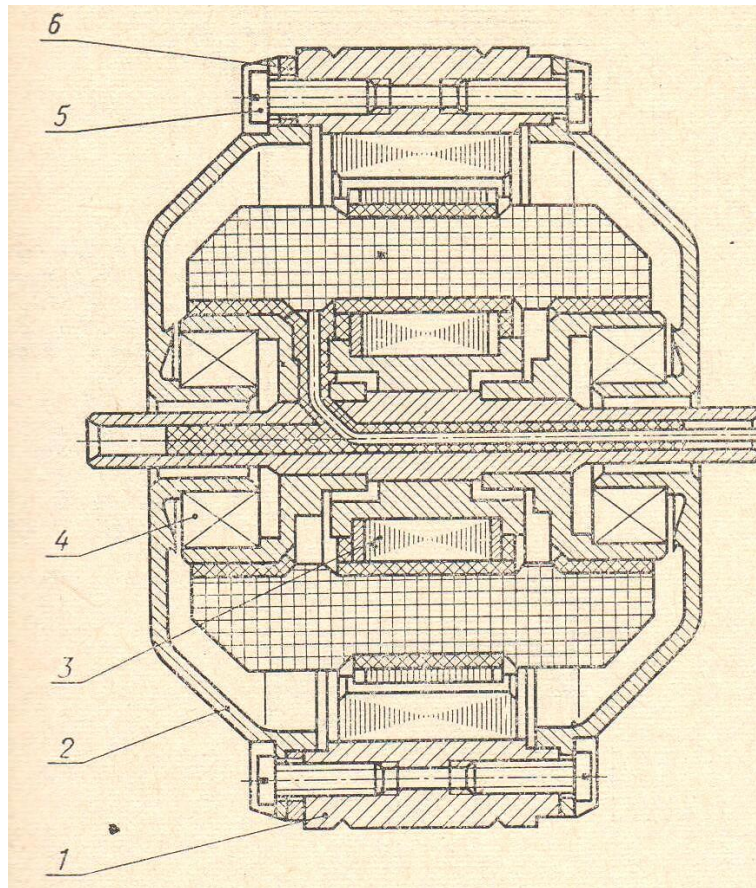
Гиродвигатель ГМС-200. 1 – ротор, 2 – крышка, 3 – статор, 4 – шарикоподшипник, 5 – винт, 6 – прокладка
